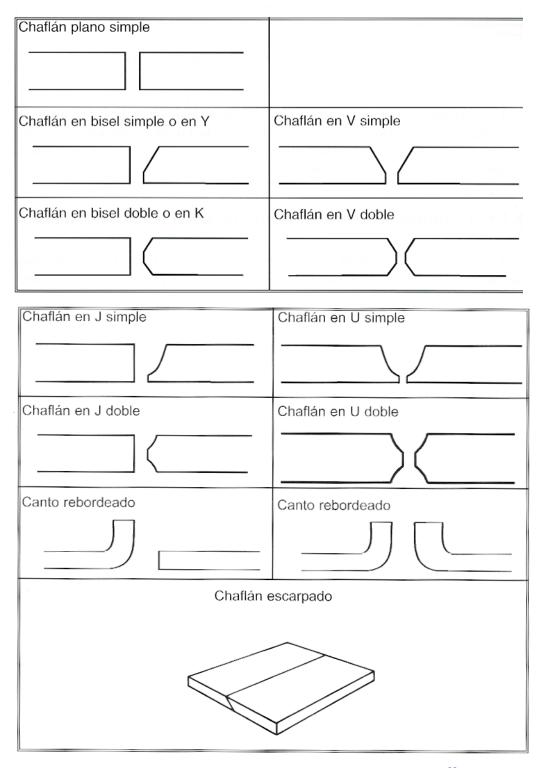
Tipos de preparación de soldaduras³³
